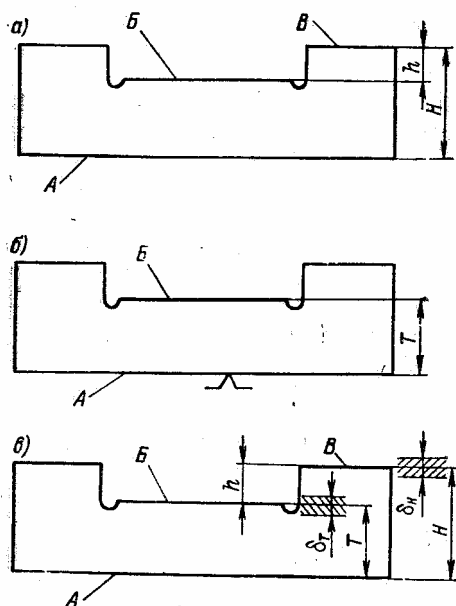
Обработка детали при несовмещении исходной базы с конструкторской:
